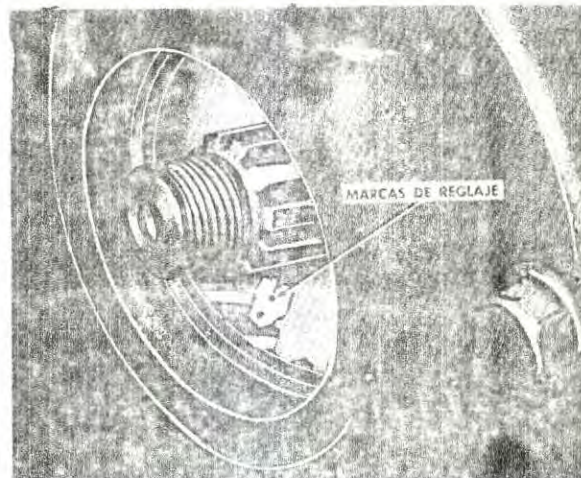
Marcas de reglaje a través del agujero de la junta estanco en la caja de engranajes.
